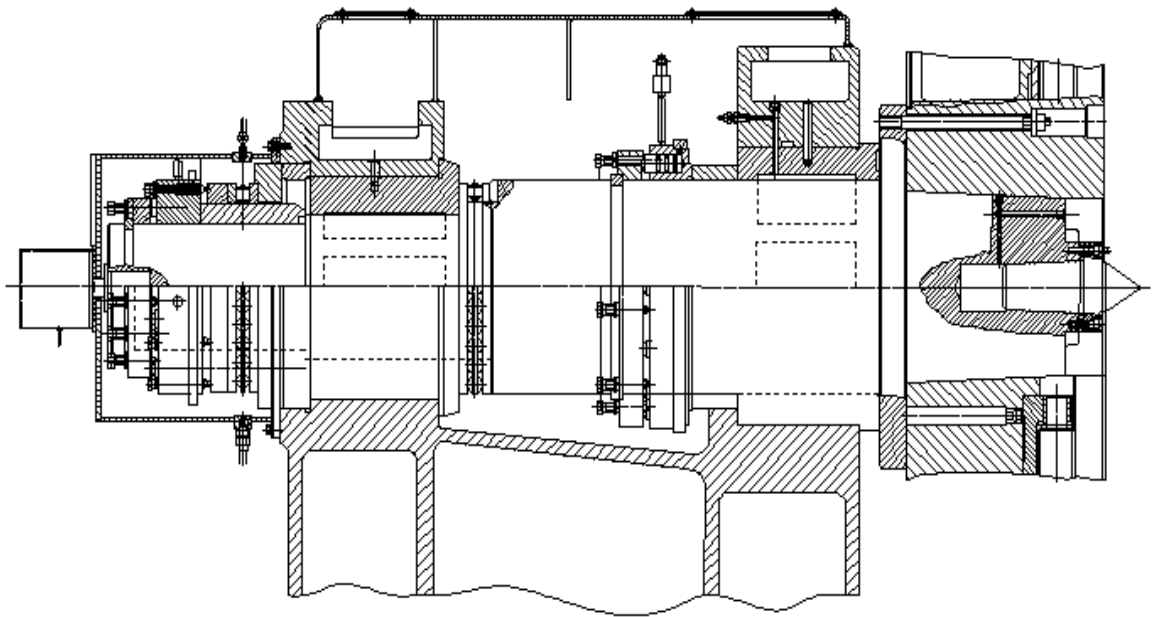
Шпиндельний вузол важкого токарного верстата з радіальними гідростатичними підшипниками й упорними підшипниками фірми FAG
